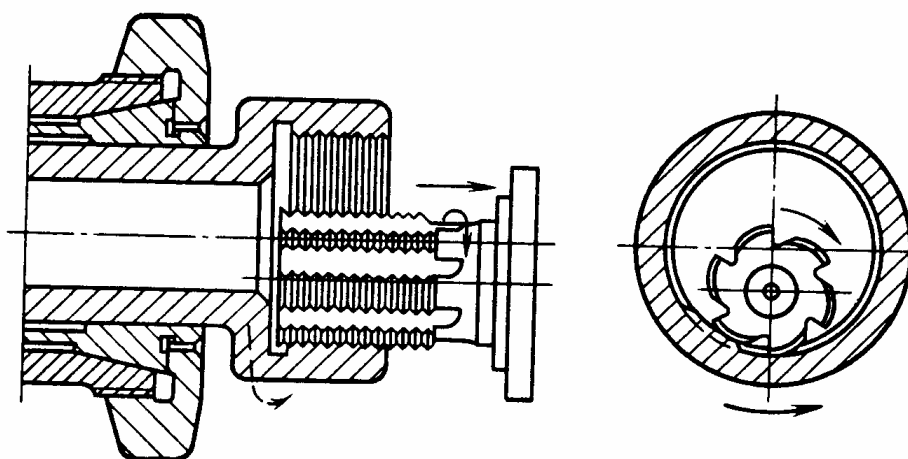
Схема фрезерування внутрішньої різьби із застосуванням гребінчастої фрези
